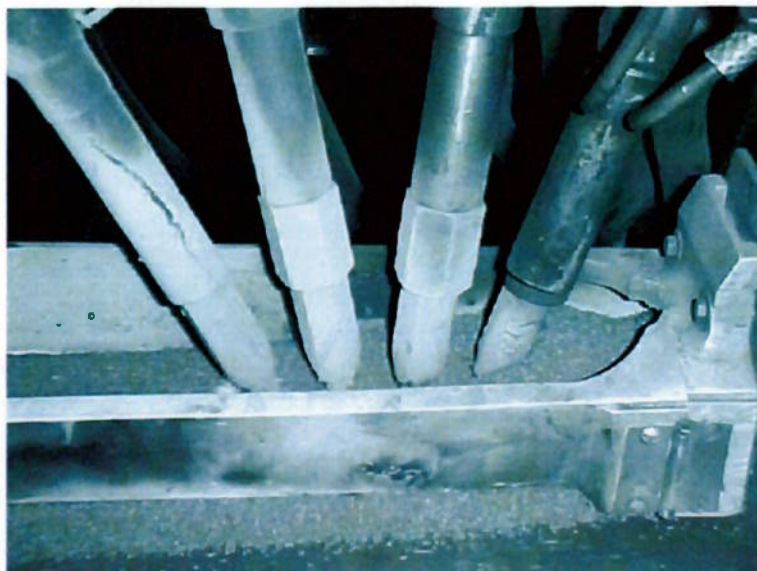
Soldagem por arco submerso, com múltiplos arames – Processo Tandem [34].
